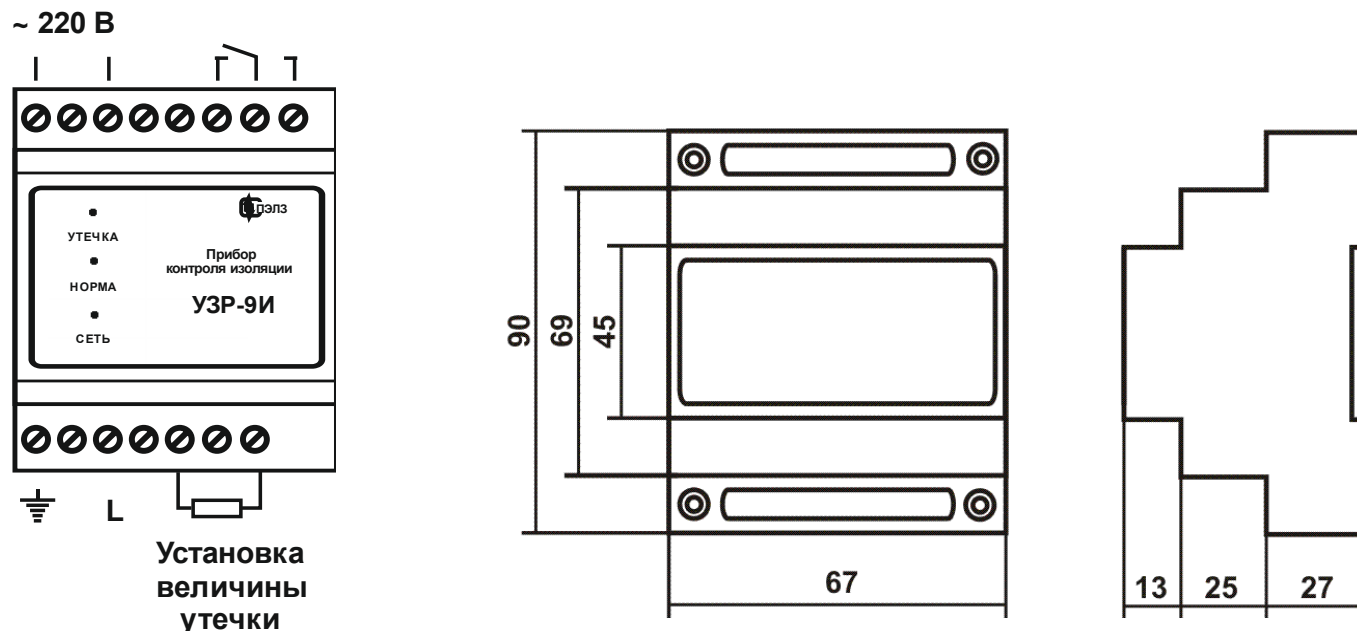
Расположение контактов на клеммниках прибора, габаритные размеры корпуса устройства.
